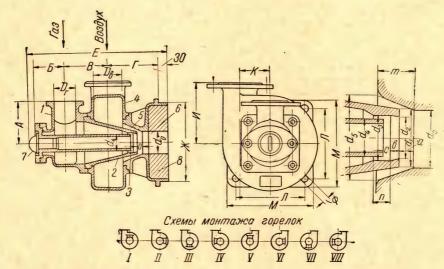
Газовая горелка с вращательным движением воздуха:
